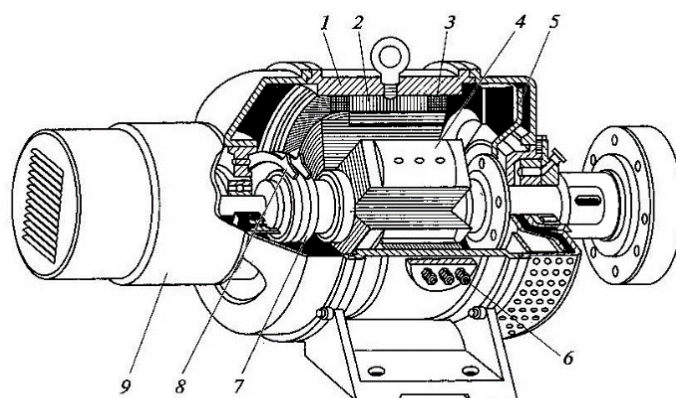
Конструкция электрокоммуницируемого двигателя: 1-корпус; 2-сердечник статора; 3-обмотка статора; 4-ротор; 5-вентилятор; 6-вывод обмоток; 7-контактные кольца; 8-щётки; 9-возбудитель; [2].
